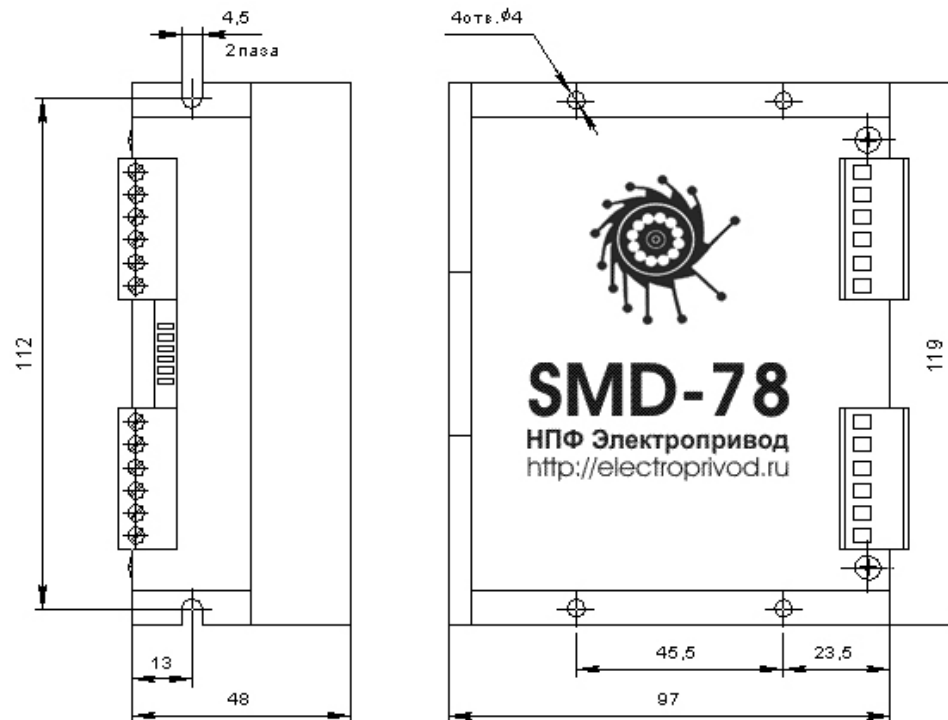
Габаритные и присоединительные размеры блока SMD-78.
